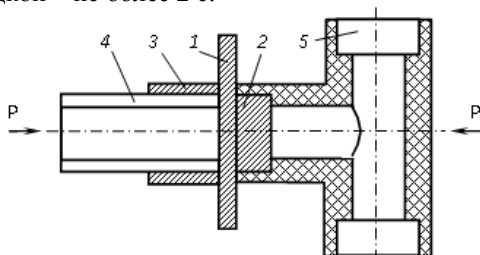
Схема нагрева при сварке в раструб
